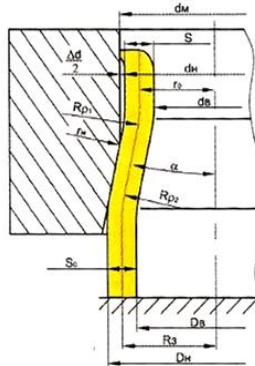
Обжим заготовки с выходом в цилиндр
